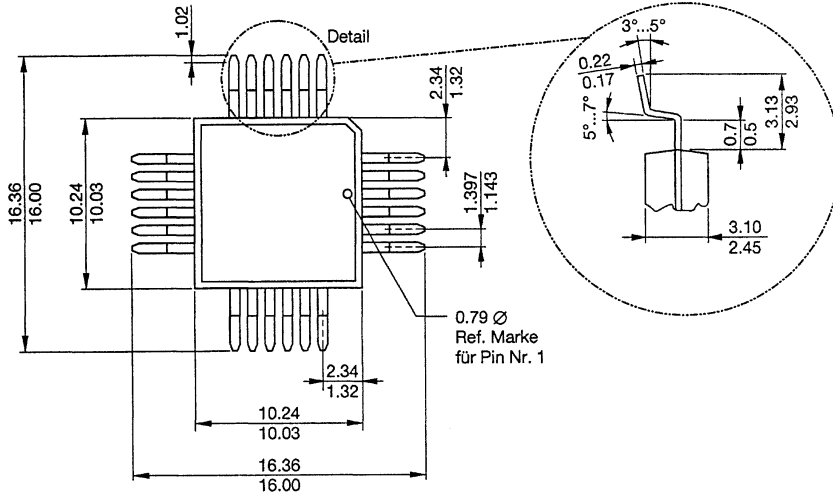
Gehäusezeichnung für ein Quad Flat Pack Gehäuse mit 24 Pins (QFP-24), Abmessungen in mm (aus [6])
